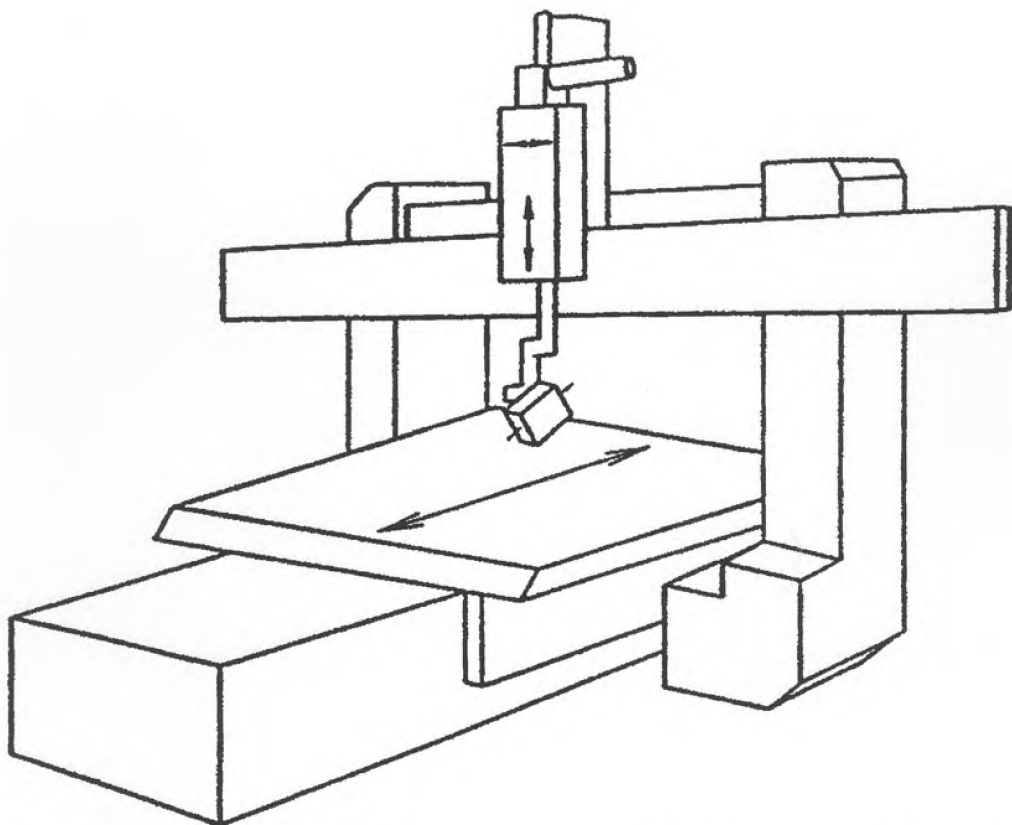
Многоинструментальный станок (подвижный стол, неподвижный портал, подвижная головка)¹
